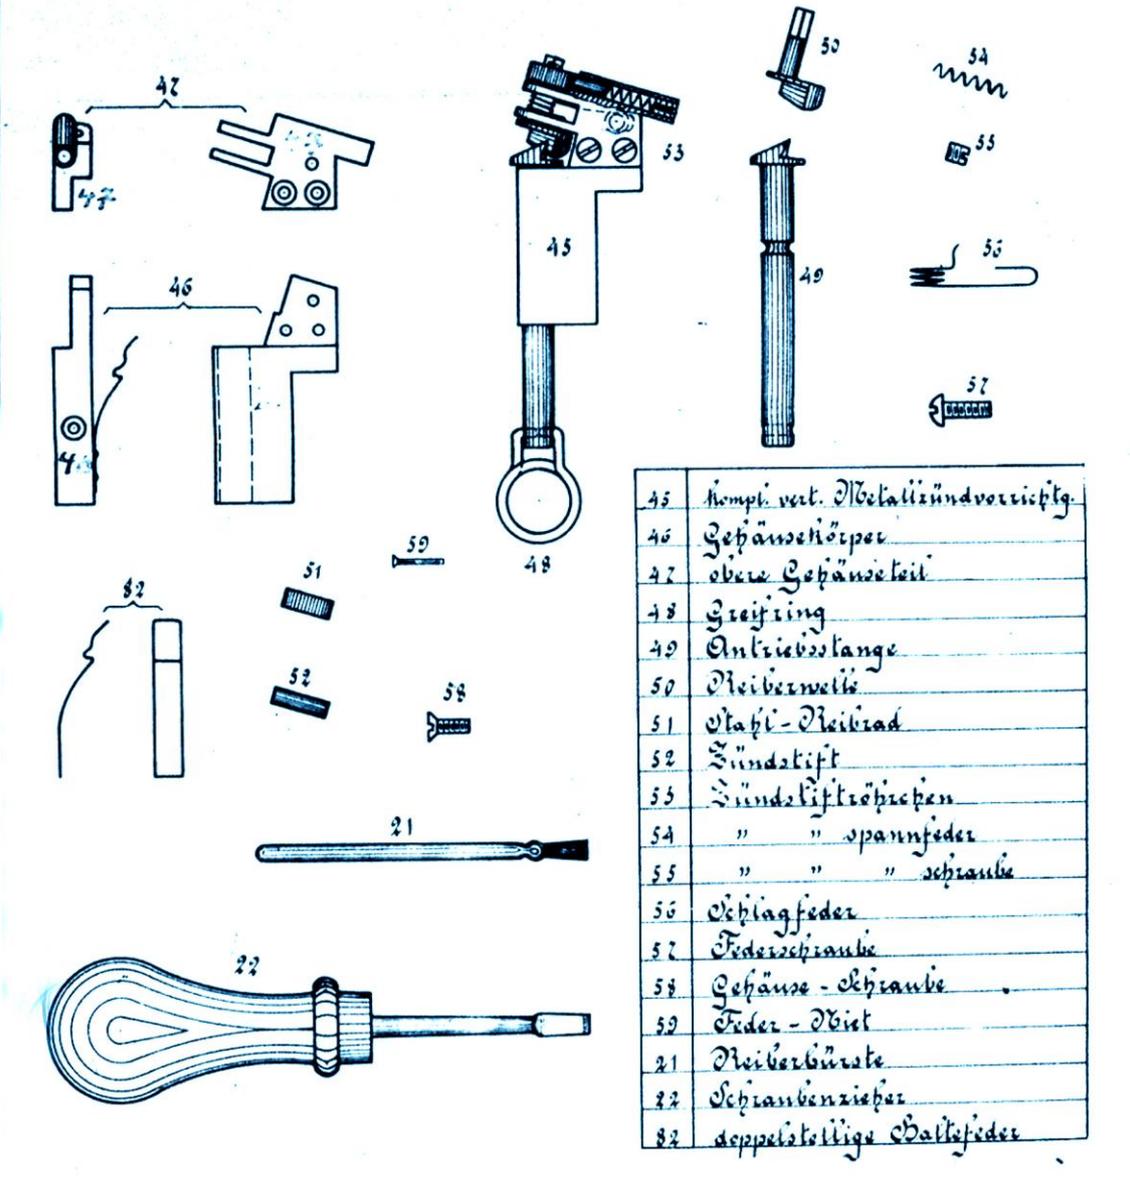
Plano de fábrica de un encendedor vertical (Arch. J.M. Sanchis)
